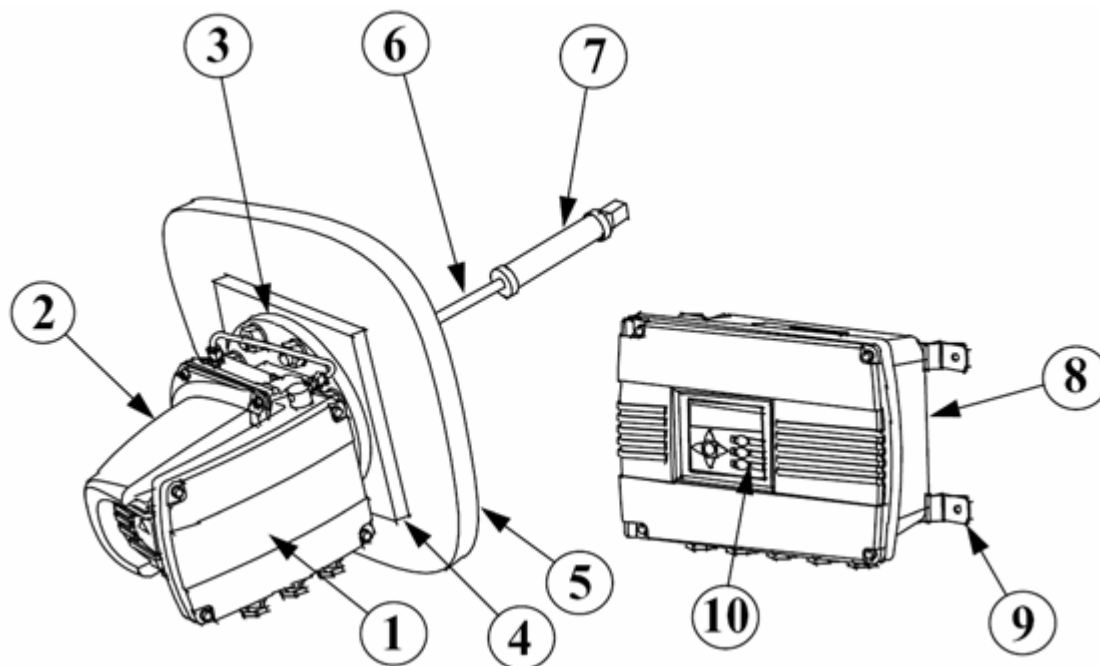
Внешний вид блоков прибора и расположение основных элементов.
